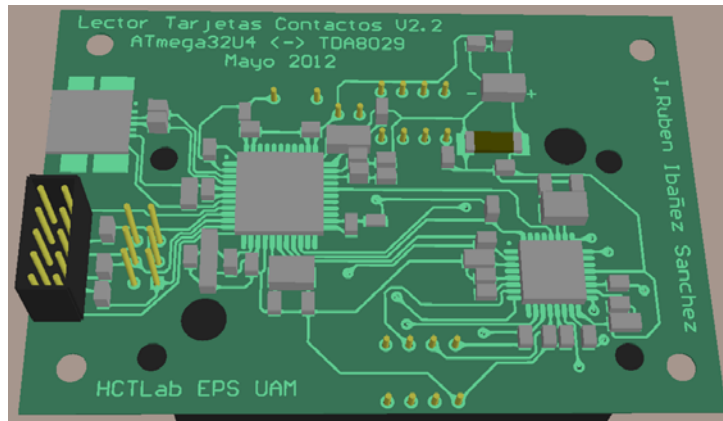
21: Vista 3D del PCB terminado con componentes.
